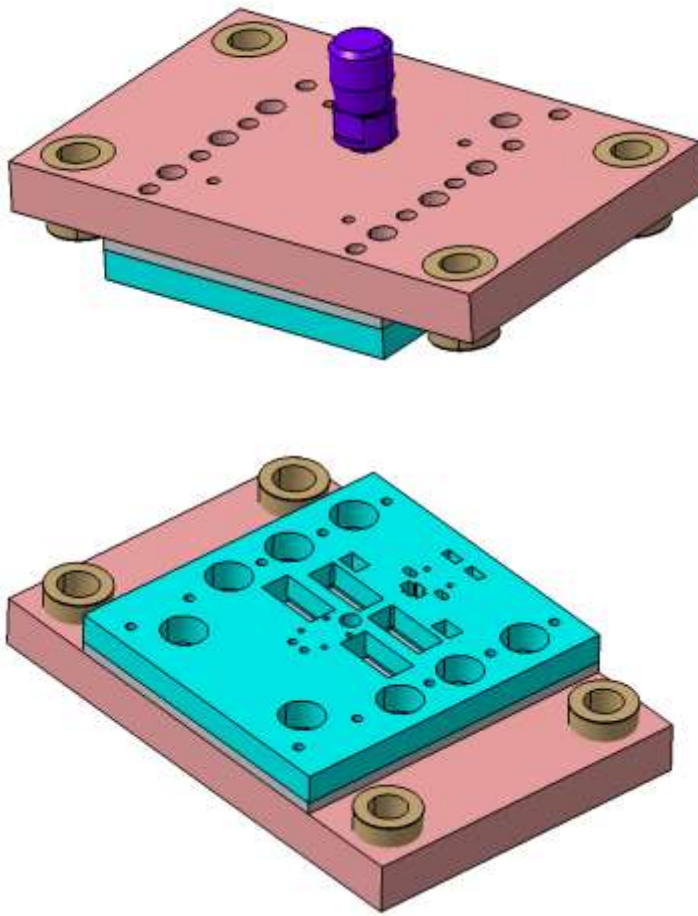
Parte superior de la matriz progresiva diseñada ensamblada (Fuente propia)
